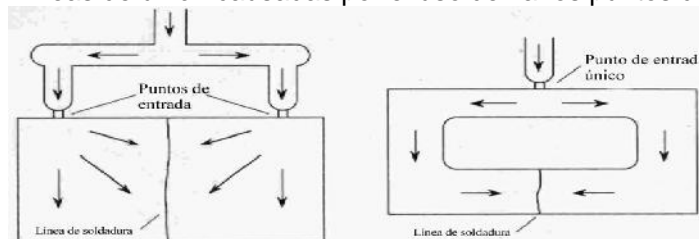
Líneas de soldadura por unión de flujos.
